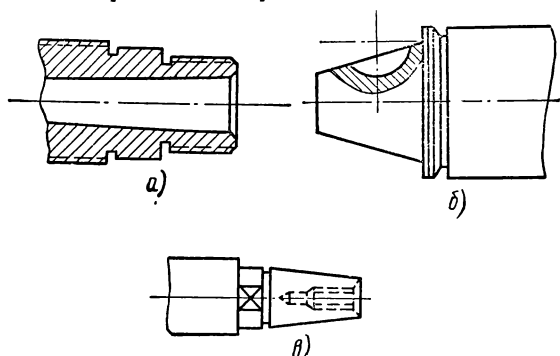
Рабочие концы шпинделей шлифовальных станков:
